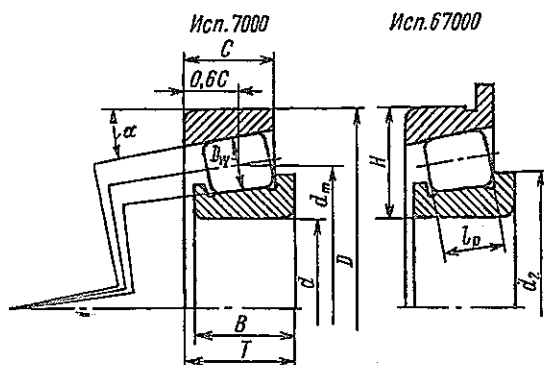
Радиально-упорные роликовые однорядные подшипники типа 7000
